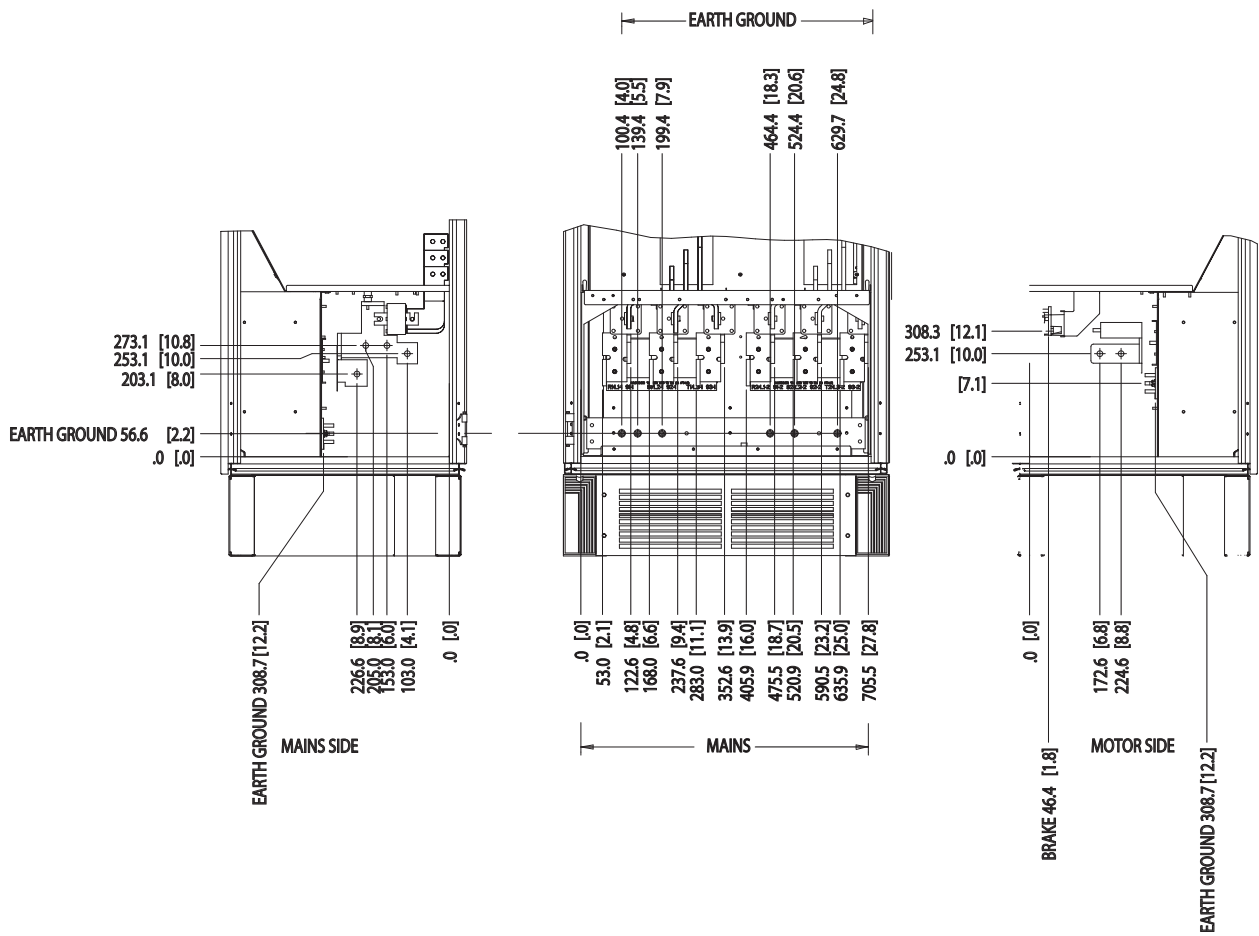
Klemposities – omvormerkast – (vooraanzicht, zijaanzicht links en rechts). De doorvoerplaat bevindt zich op 42 mm onder niveau '0'.
